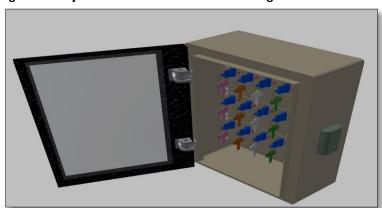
Projeto da Estrutura do Chaveiro Inteligente
